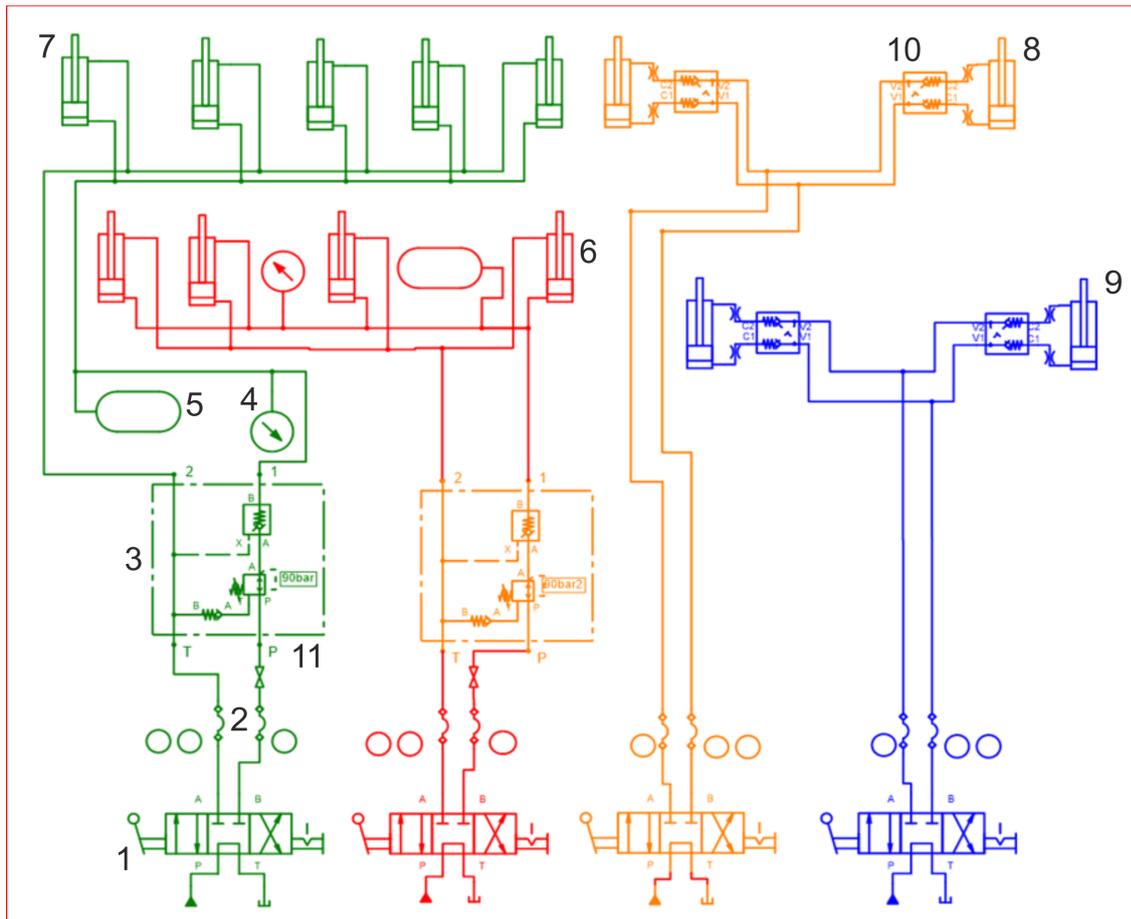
Schéma hydraulique de la machine DIGGER 3 N
